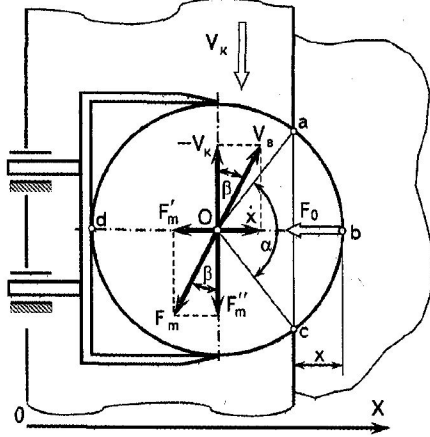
Розрахункова схема до перевантаження виробу циліндричної форми з рухомою опорною площиною на нерухома за умови $x \leq r$
